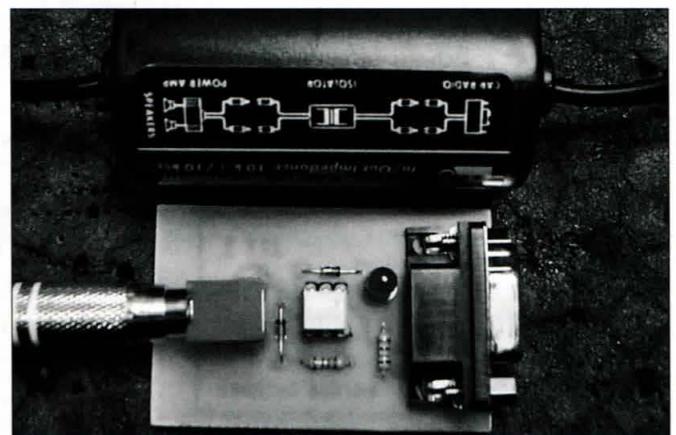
Montaje final de la versión reducida del adaptador para tarjeta de sonido.
